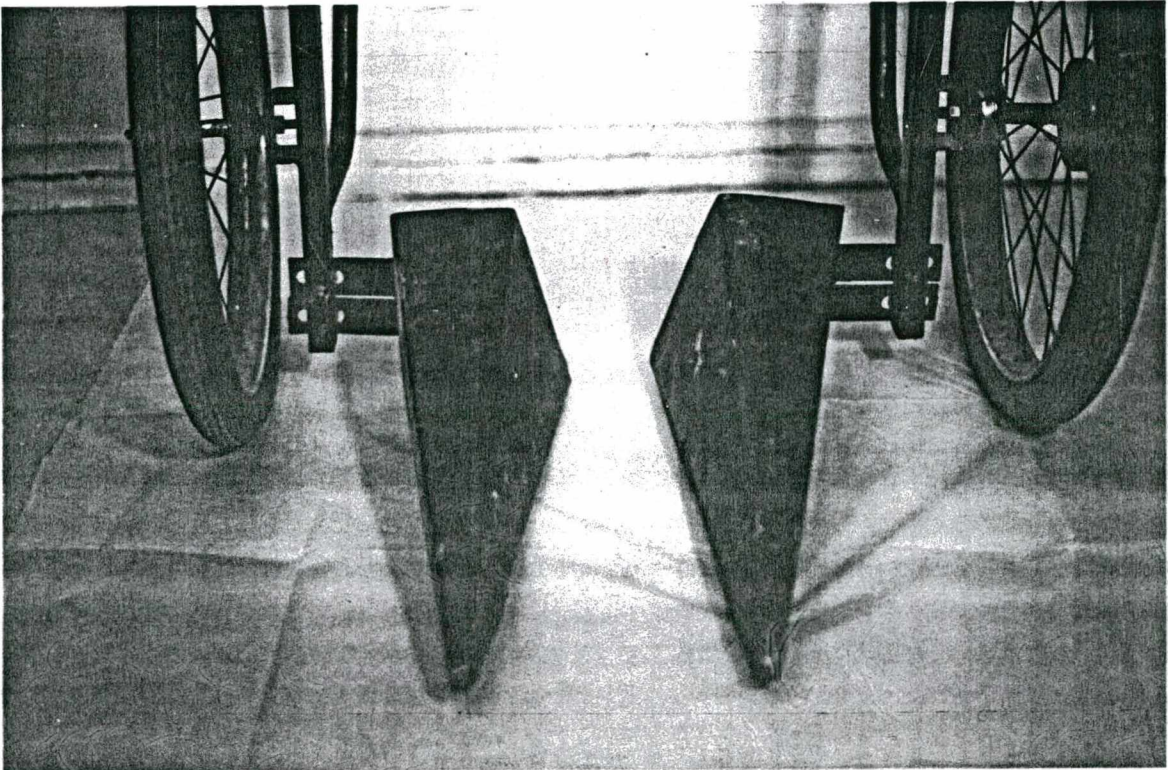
b: Levantador com 3 faces e face interna a 70° .
